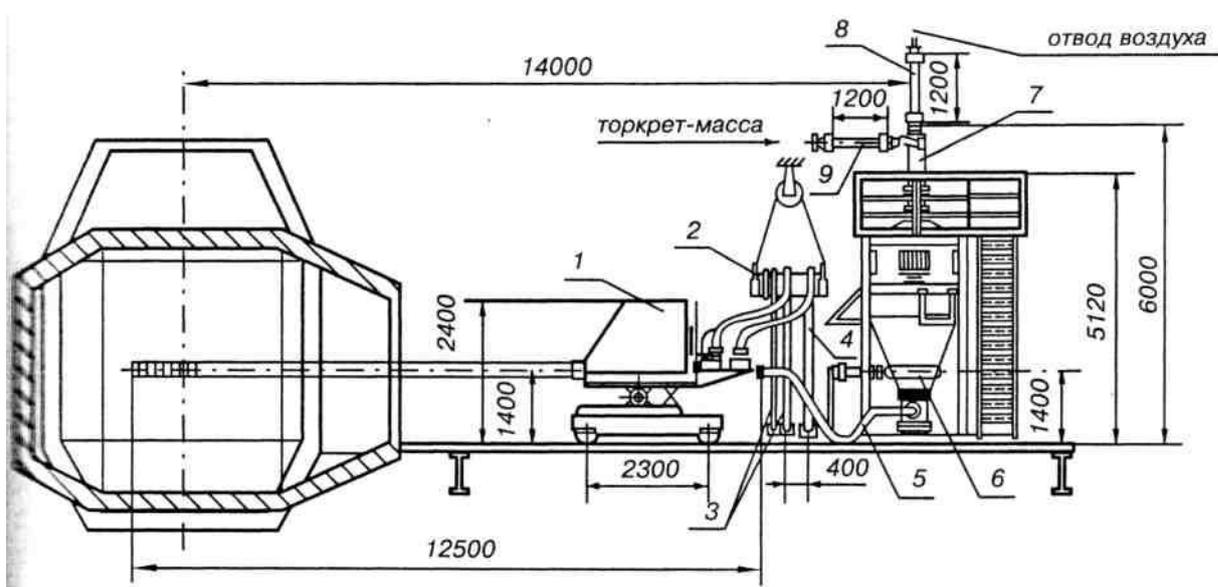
Размещение комплекса оснащения для горизонтального факельного торкретирования. 1 – торкрет-машина; 2 – подвеска шлангов; 3 – гибкие рукава подачи воды; 4 – гибкий рукав подачи кислорода; 5 – гибкий рукав подачи торкрет-массы; 6 – камерный питатель; 7 – циклон; 8 – трубопровод сбрасывания воздуха; 9 – трубопровод подачи торкрет-массы.
